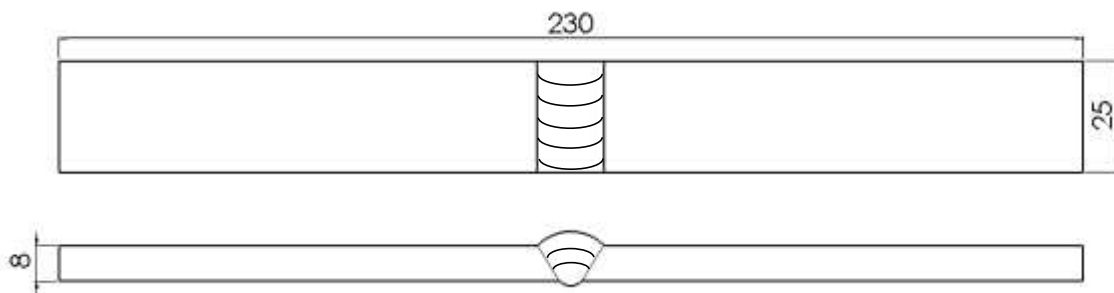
Dimensiones, probeta de ensayo de tracción.
